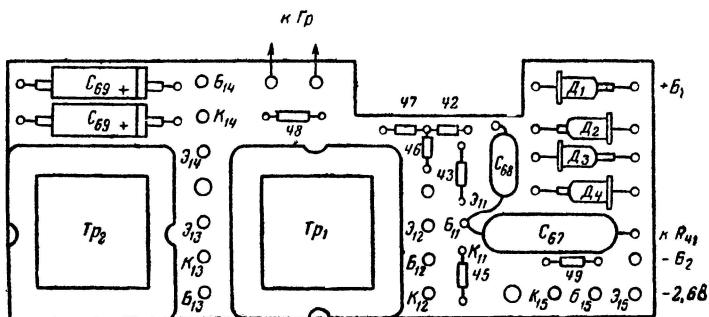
Блок усилителя низкой частоты и стабилизатора напряжения.
